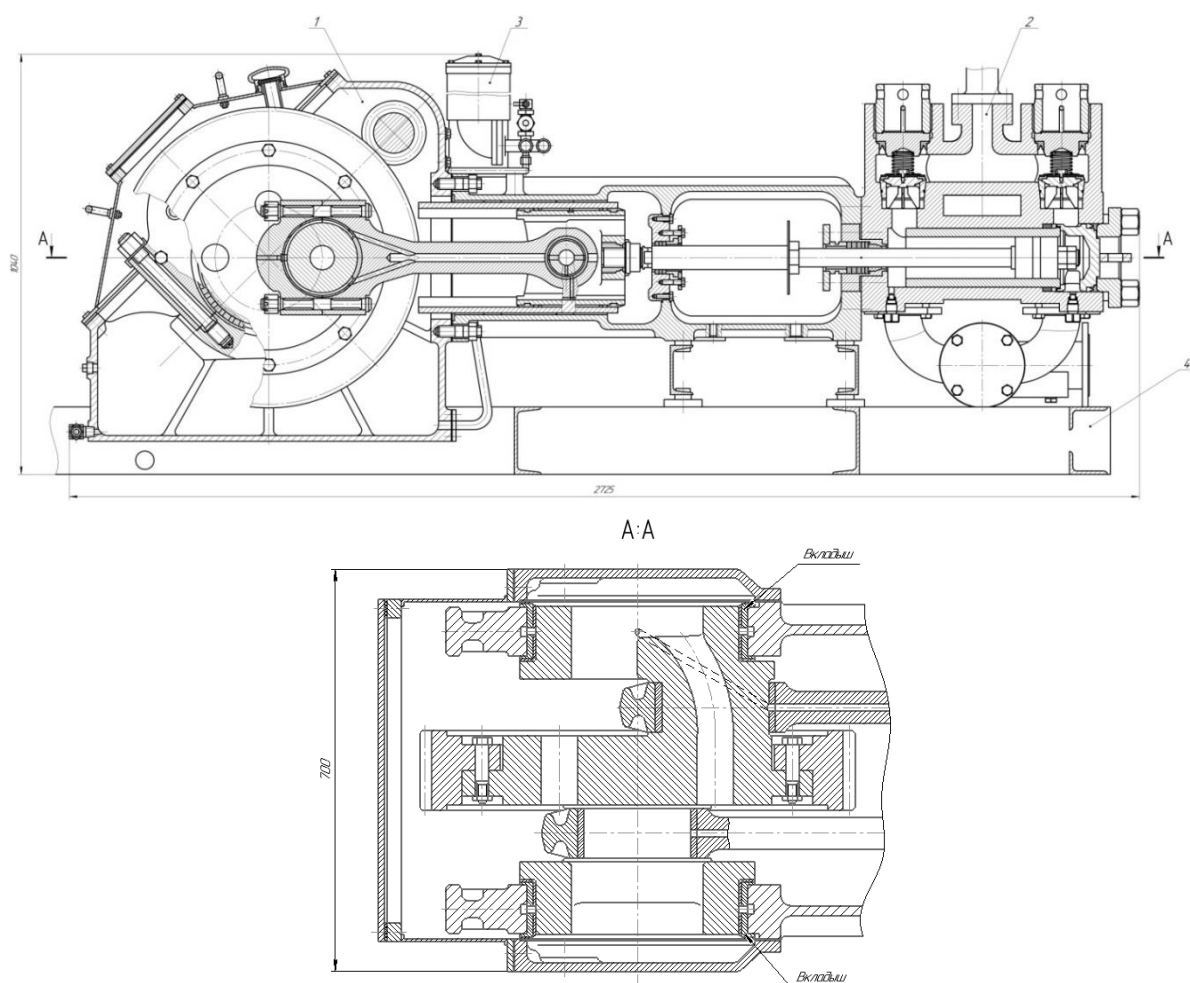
Сборочный чертеж бурового насоса НБ-125
